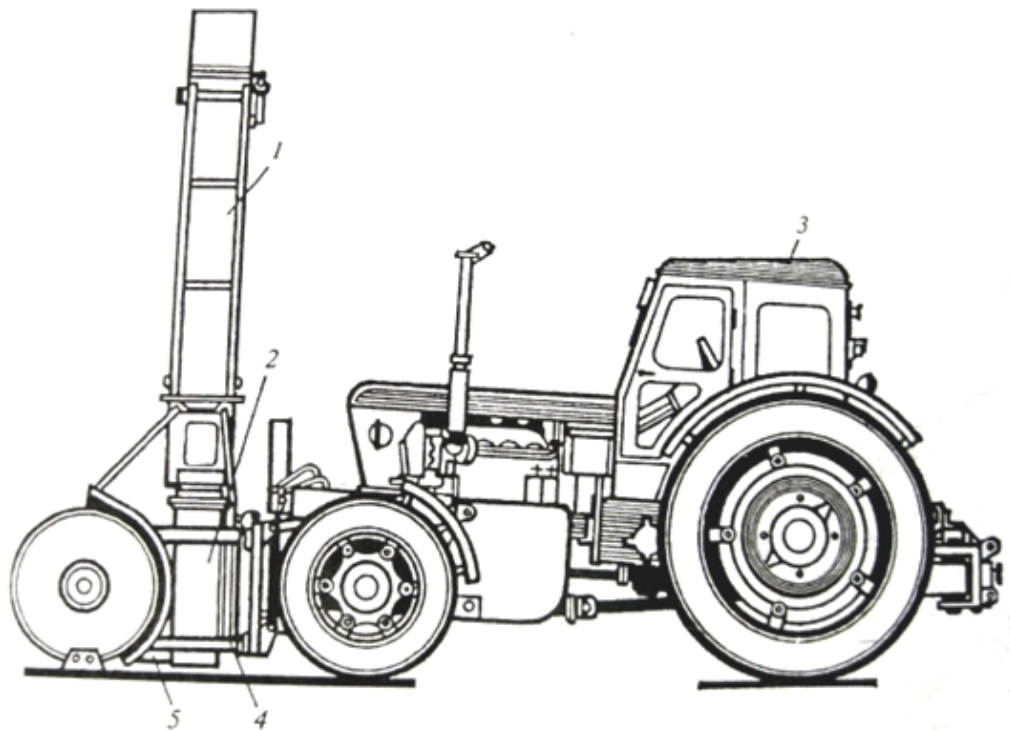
Снегоочиститель с фрезерно-роторным рабочим органом
